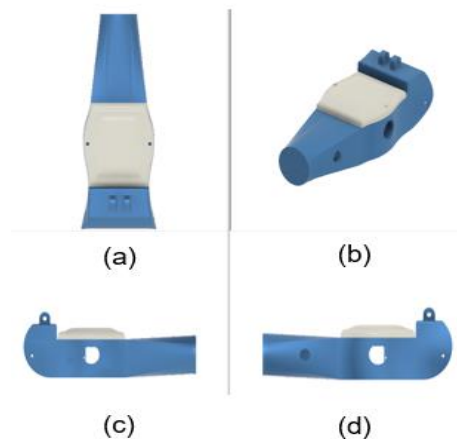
Diseño antebrazo. a) Vista superior. b) Vista ortográfica. c) Vista izquierda. d) Vista derecha.
